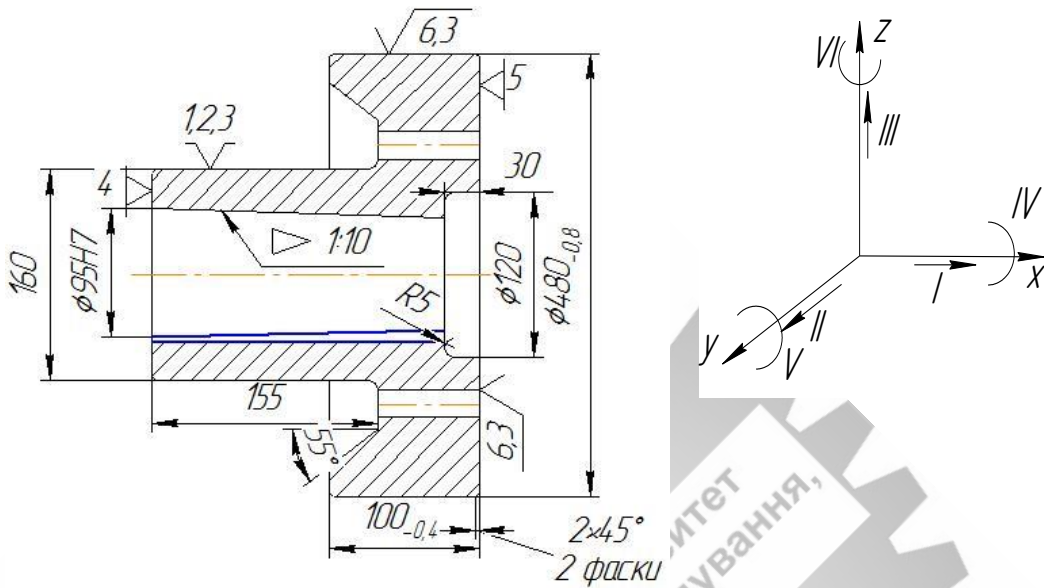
Схема базування заготовки на протяжній операції
